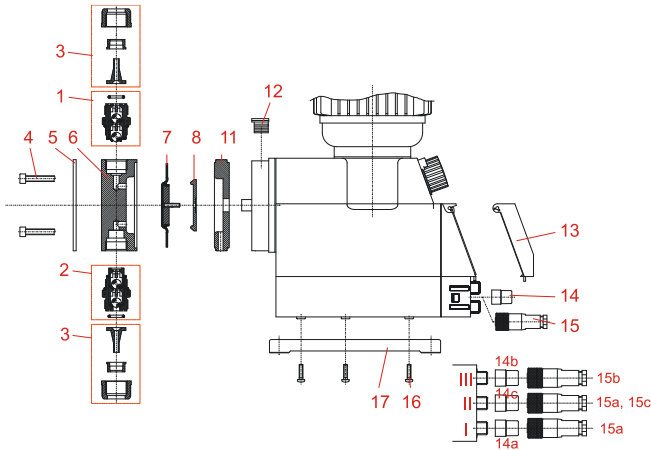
Vue éclatée / Liste des pièces Type 00160, Type 00250, Type 00540
